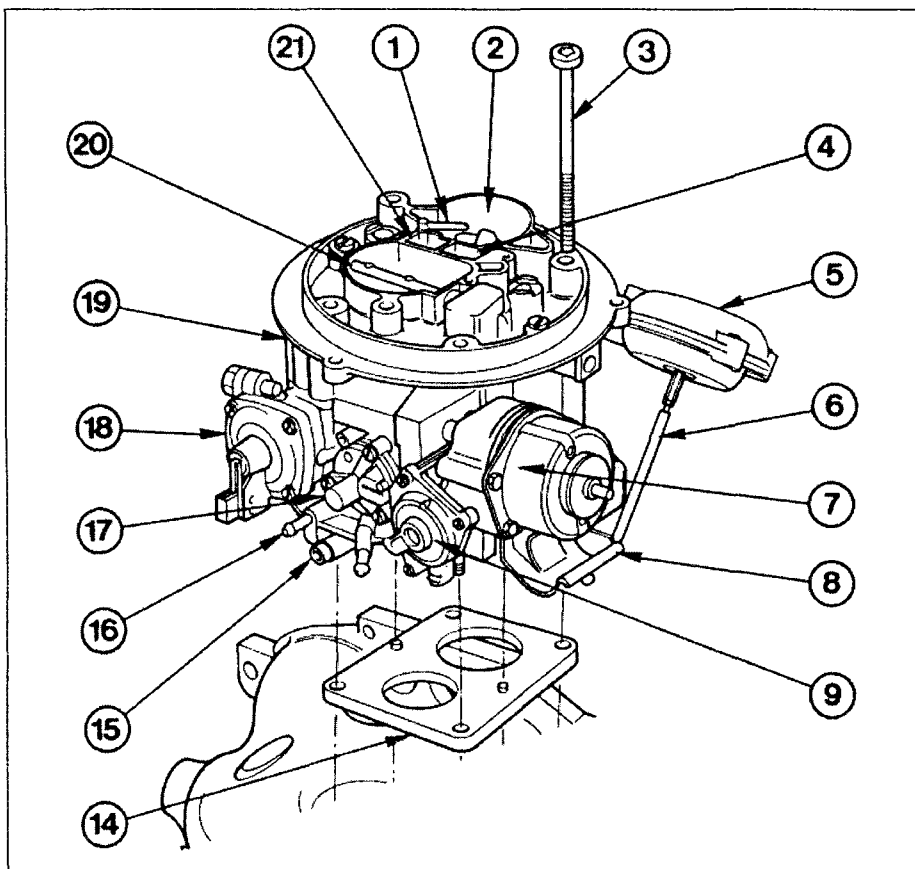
Карбюратор TLDM 26/32 - двигатель 2.0 л
